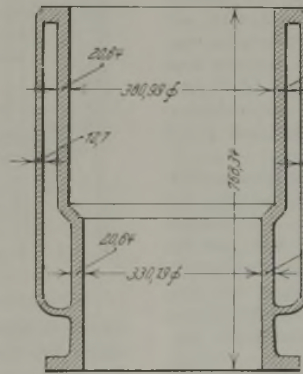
Deutscher Kompressorzylinder. Gewicht = 3048 kg.
